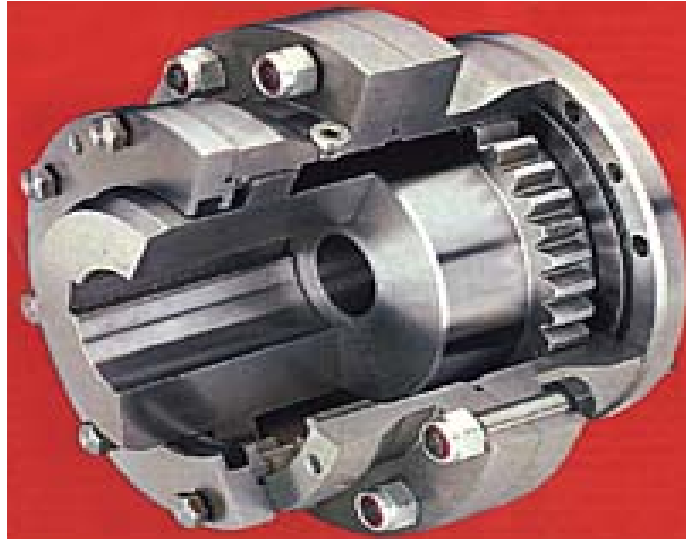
Acoplamientos flexibles de engranaje [6].
